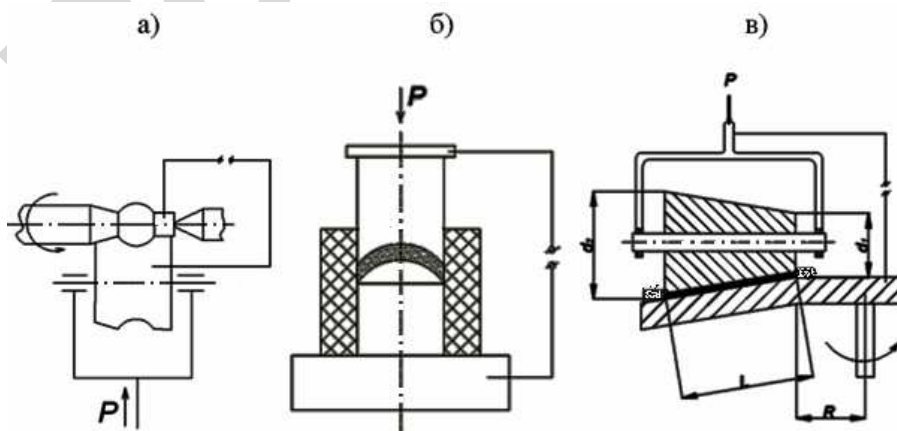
Схемы нанесения покрытий на детали сложного профиля:
